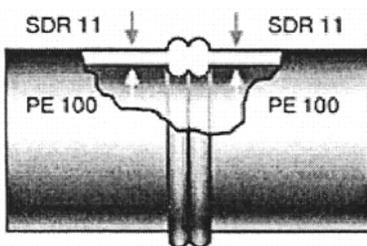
Внешний вид сварного соединения
